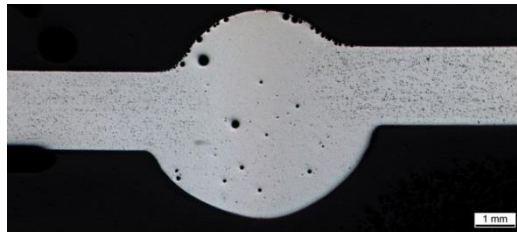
Микрошлиф сварного шва, $V = 3,5$ м/мин
